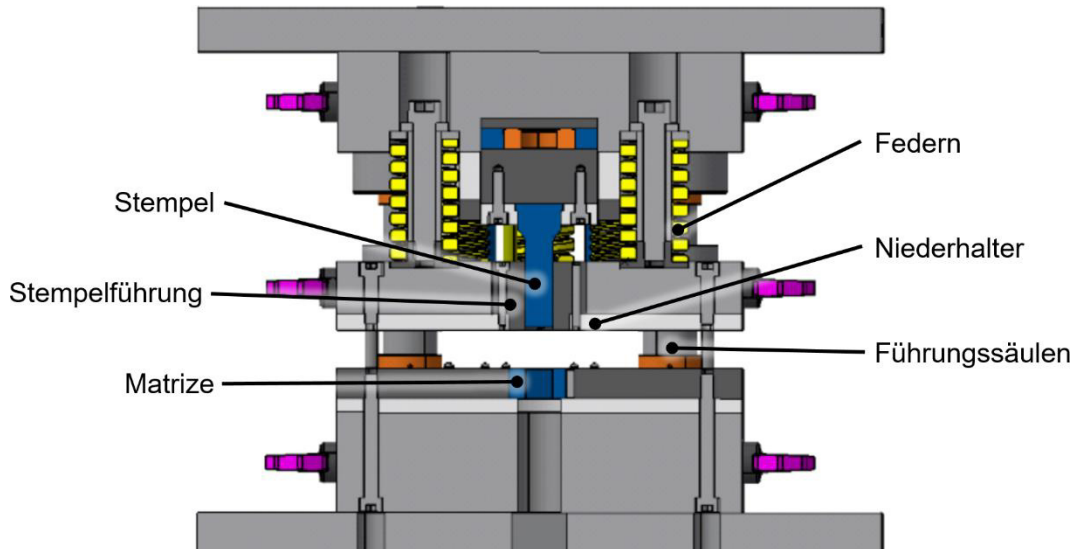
Schnitt durch das Universal-Scherschneidwerkzeug
